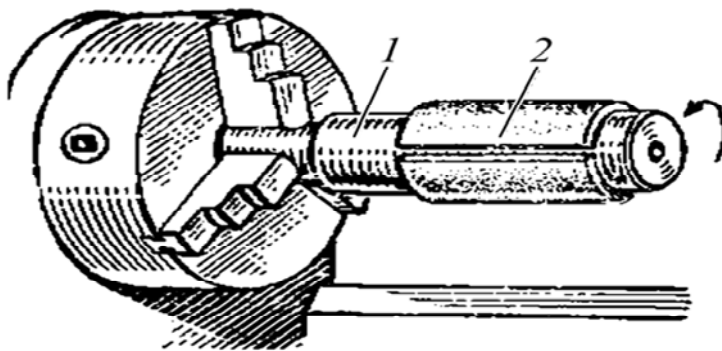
Инструмент для притирки отверстий на токарном станке
